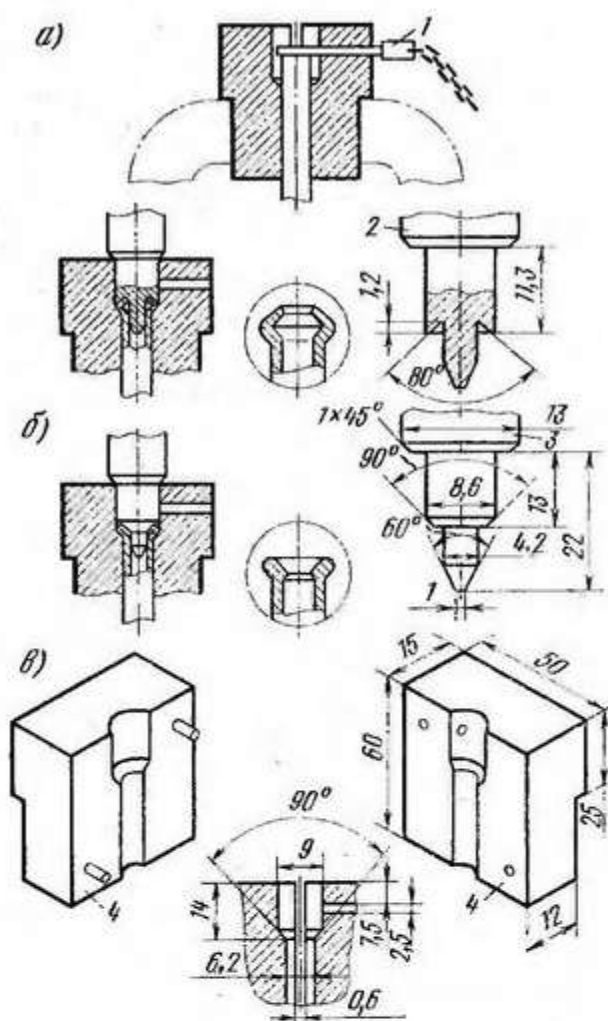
Двойная развальцовка трубок гидравлического привода тормозов:
